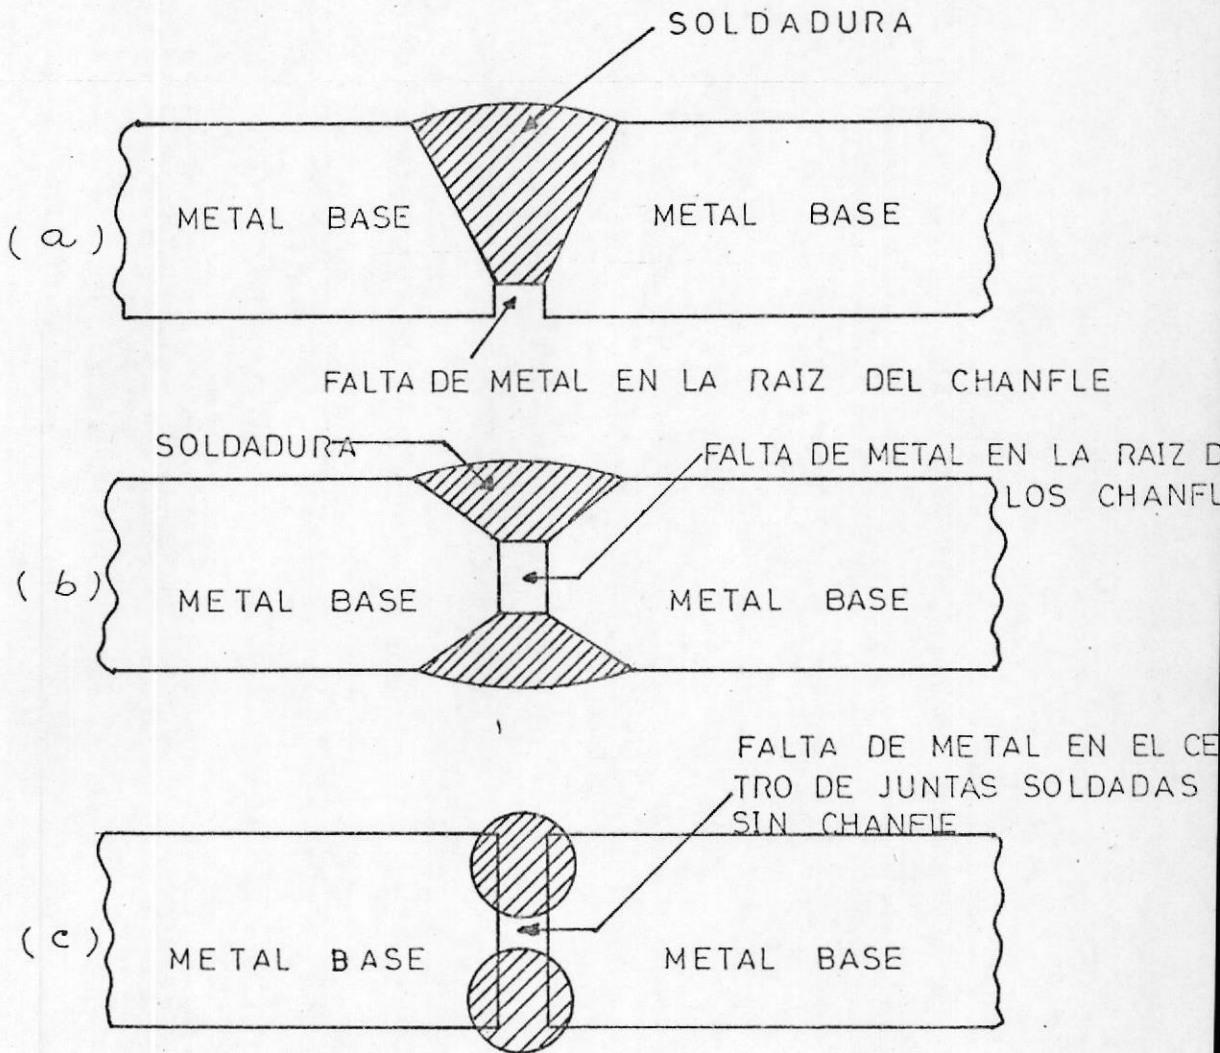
FALTA DE PENETRACION EN PROCESOS DE SOLDADURA AL ARCO (10)
